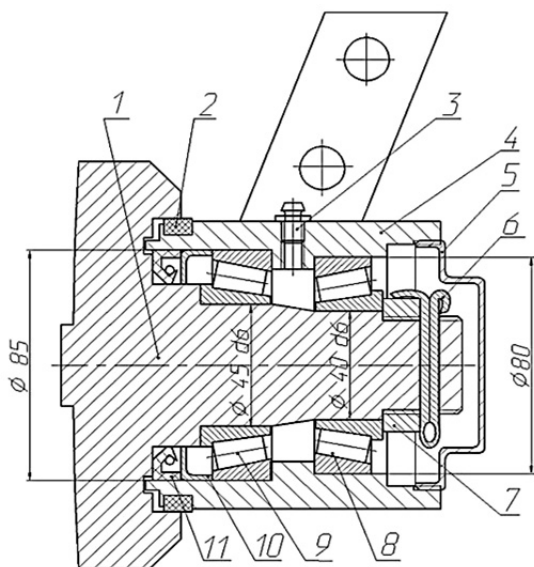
Ступица АДУ-6 АКД с подшипниками качения:
